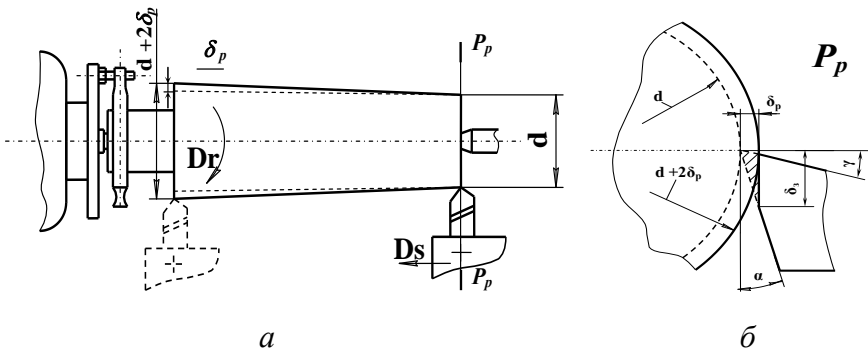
Схема впливу зношування різця на розмір обробленої поверхні
